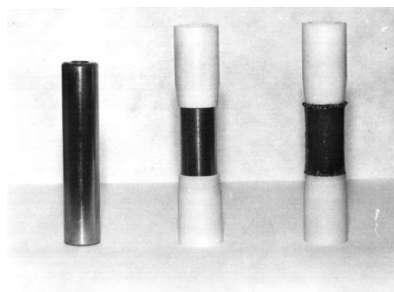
Общий вид образцов для определения прочности сцепления покрытия с основой
